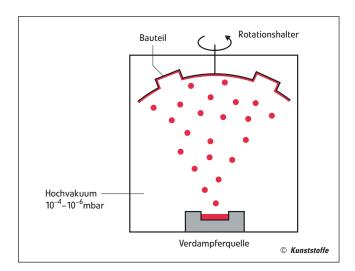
PVD-Verfahren (Physical Vapor Deposition): Der Scheinwerfer wird auf einem Rotationshalter befestigt und unter Hochvakuum mit Aluminium bedampft
